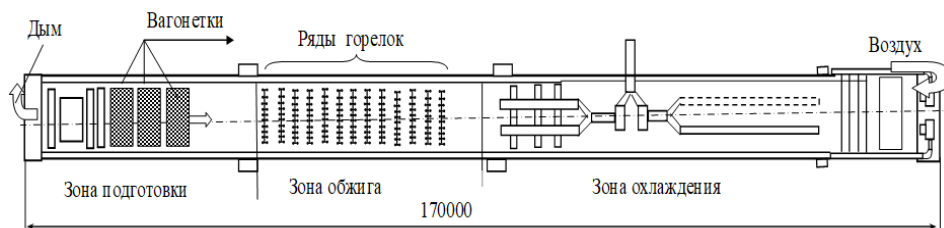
Упрощенная схема туннельной печи: вид сверху Fig 1. Simplified diagram of a tunnel kiln: top view
